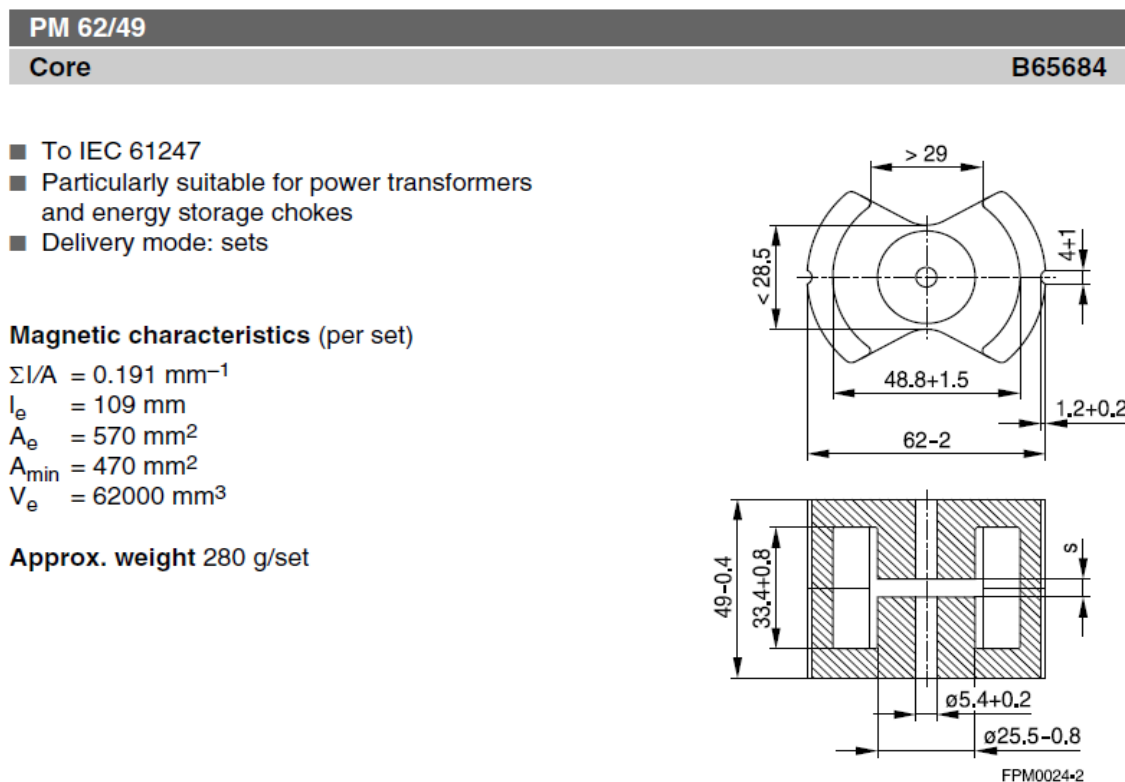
Dimensiones del núcleo de ferrita PM62/49
